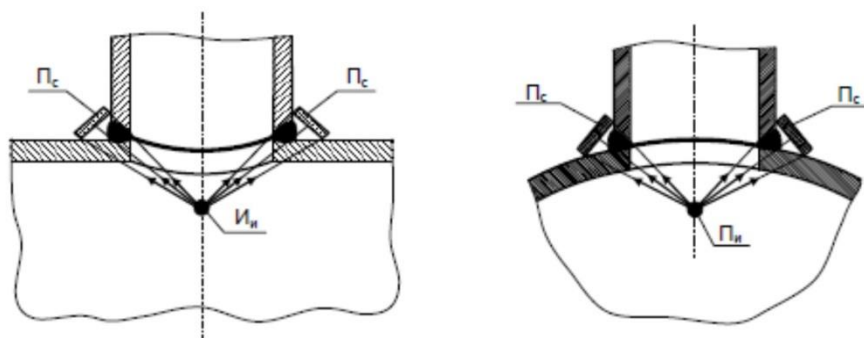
Схема просвечивания углового сварного соединения изнутри трубы за одну установку источника излучения
